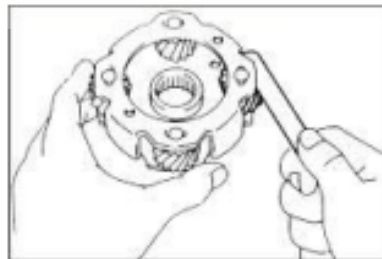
Mengukur Diameter Dalam *Sun Gear
